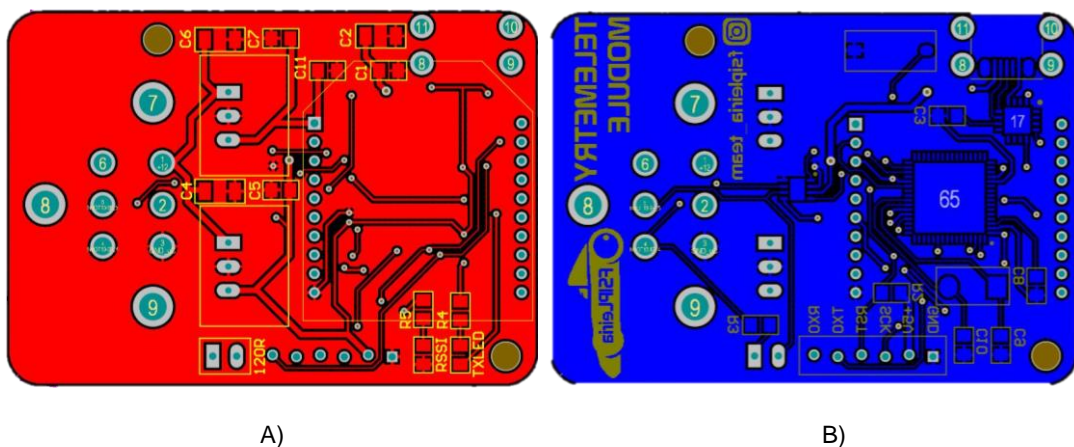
Design Final da PCB do Módulo da Telemetria - 2D. A) Top Layer, B) Bottom Layer.
